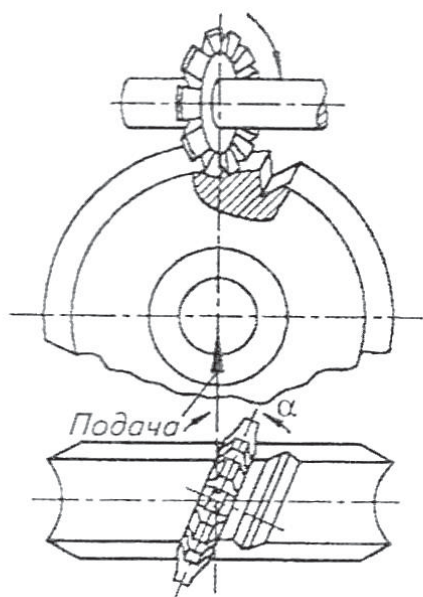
Схема нарезания зубьев червячного колеса дисковой модульной фрезой
